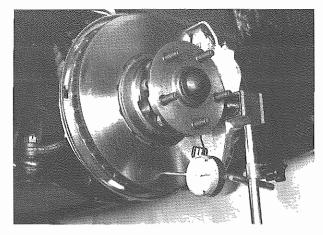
Fissare il portacomparatore Fiting dial gauge holder
